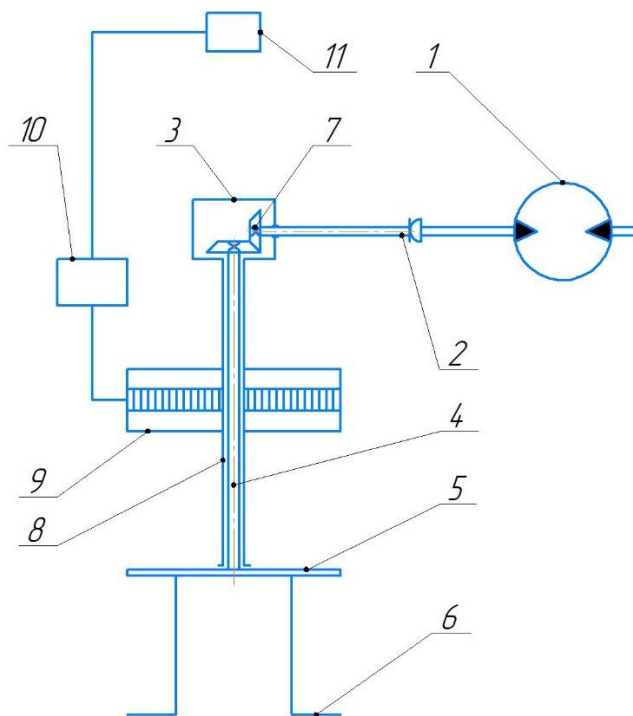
Ротаційний робочий орган культиватора: 1 – гідромотор; 2 – карданний вал; 3 – редуктор; 4 – вал; 5 – диск; 6 – ножі; 7 – шестерня; 8 – труба; 9 – електропривід; 10 – контролер; 11 – відеокамера.
